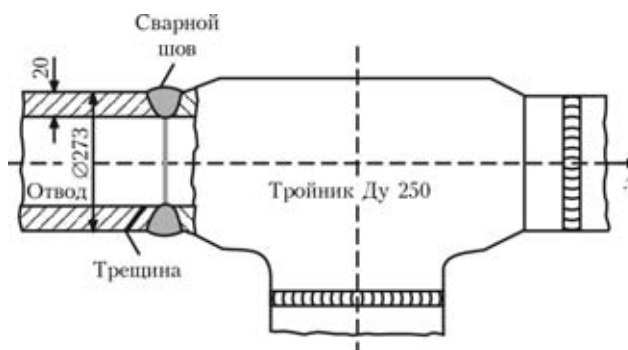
Схема трещины в сварном соединении отвода с тройником
